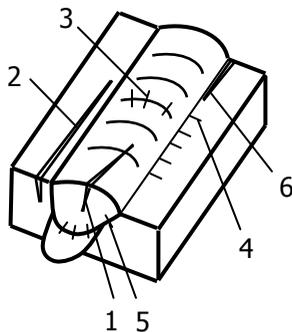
Трещины в сварном соединении: 1 и 2 – продольные в шве и околошовной зоне; 3-5 – поперечные трещины; 6 – трещина вдоль линии сплавления
